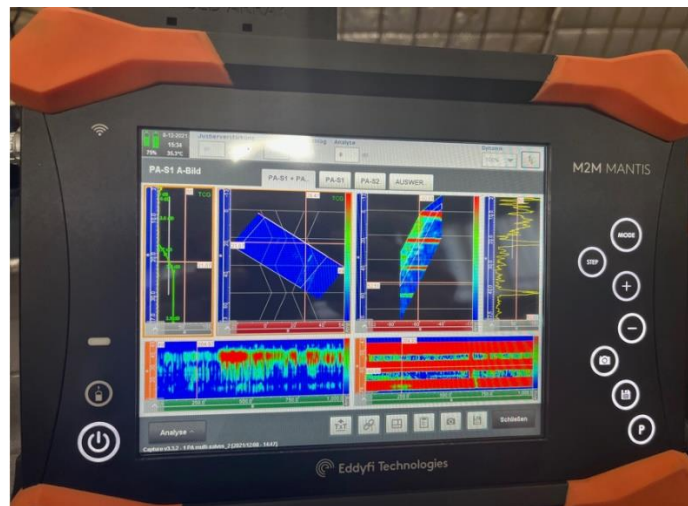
MANTIS-Prüfgerät mit Visualisierung der Schweißnaht
